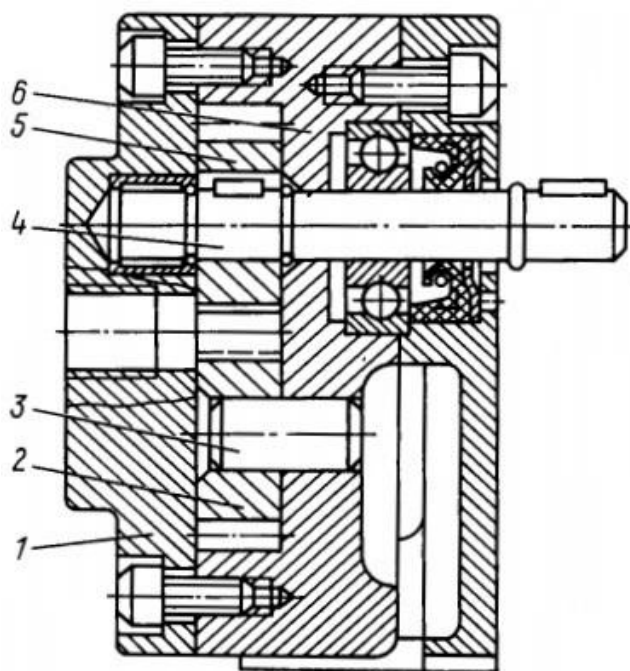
Чертеж шестеренного насоса типа Г11-1 (сечение по осям вращения шестерней): 1 – крышка; 2, 5 – ведомая и ведущая шестерни; 3 – ось; 4 – вал, 6 – корпус
